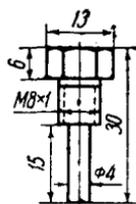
Дет. № 01-6н. Ось вилки поплавка
